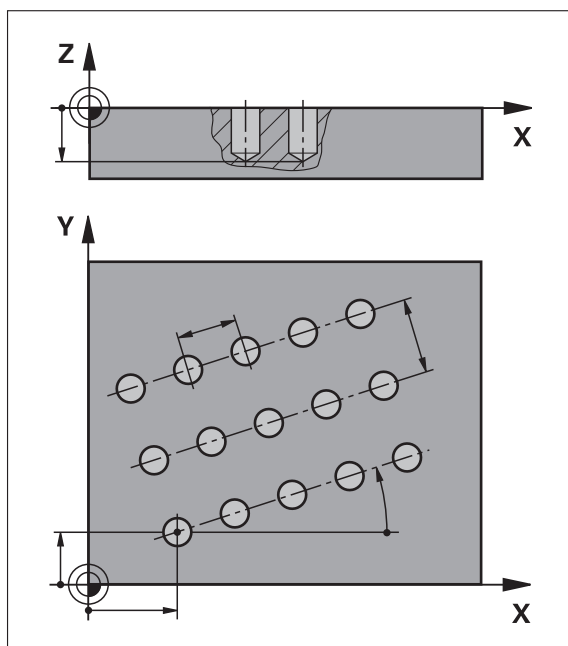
Схематическое представление кадра Ряд из отверстий
